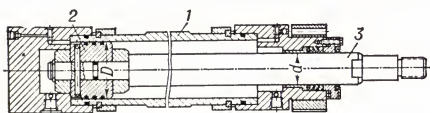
Силовой гидроцилиндр: 1 — цилиндр; 2 — поршень; 3 — шток.
